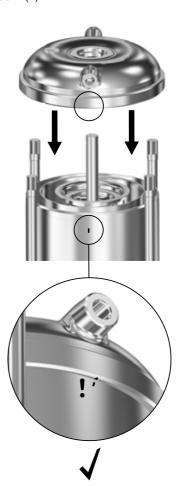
Совмещение крышки головной части (2) и цилиндрического кожуха (55)
